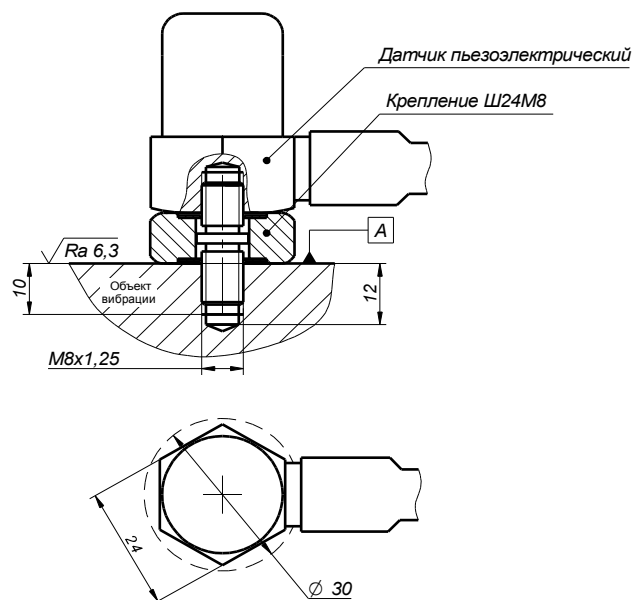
Установка датчиков с корпусом типа ТЗМ4
